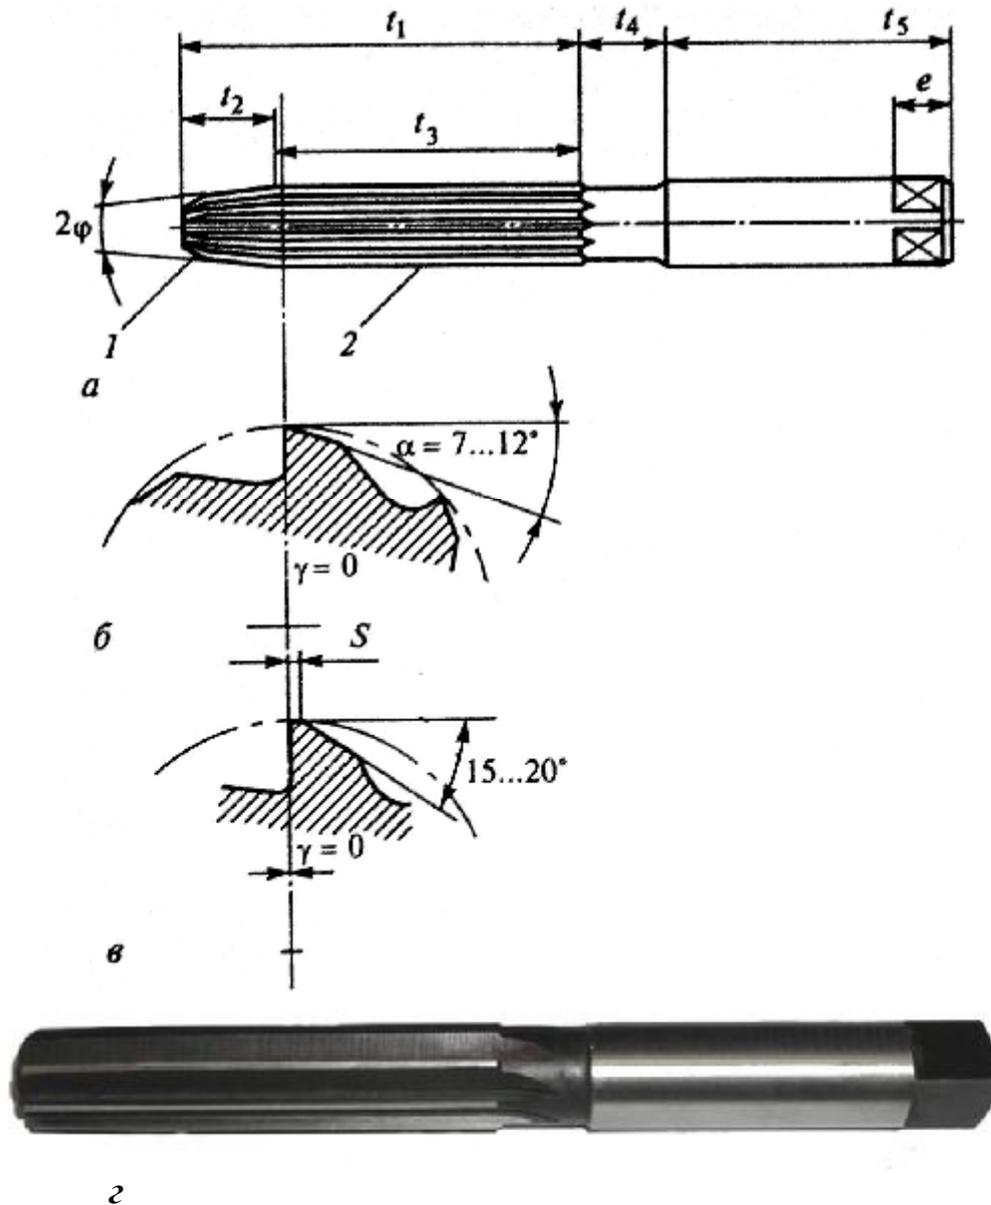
Развертка цилиндрическая: *a* – элементы развертки: l_1 – рабочая часть; l_2 – режущая часть; l_3 – калибрующая часть; l_4 – шейка; l_5 – хвостовик; e – квадрат; *б* – зубья в поперечном сечении (режущая часть); *в* – зубья в поперечном сечении (калибрующая часть); s – ленточка; *z* – развертка цилиндрическая
